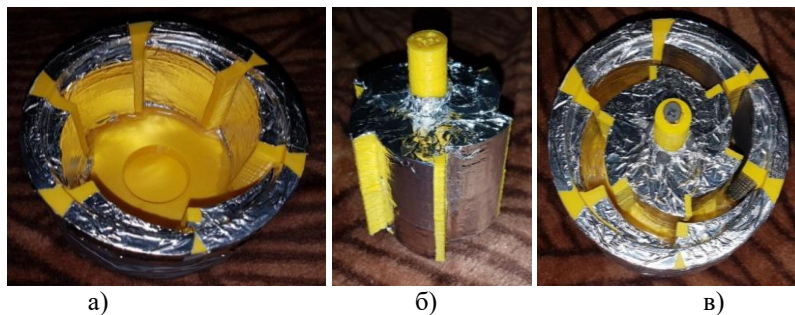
Нанесение токопроводящей поверхности: а – на лопасти корпуса; б – на лопасти ротора; в – установка ротора в корпус.
